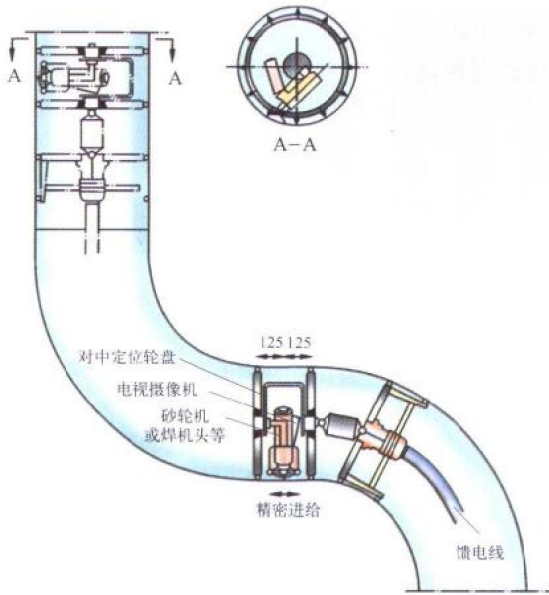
核辐射环境条件下管道内焊接修理用灵巧焊接设备
